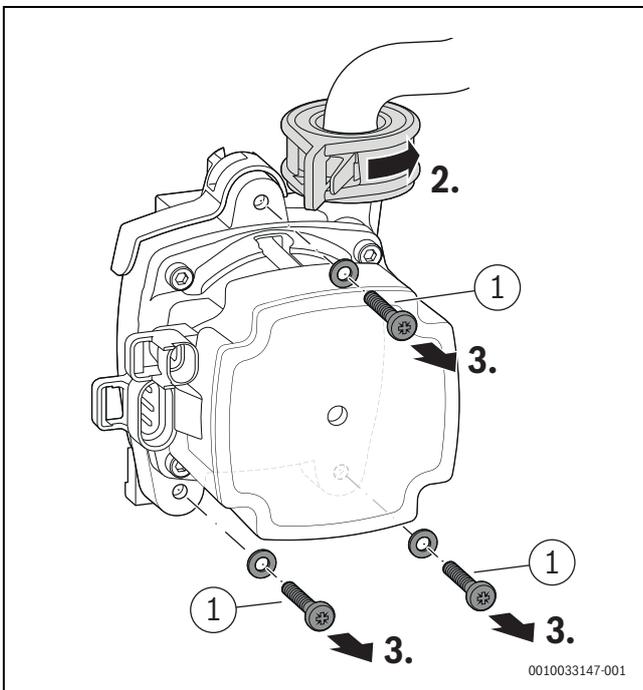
Déverrouiller la pompe de chaudière et retirer les vis
